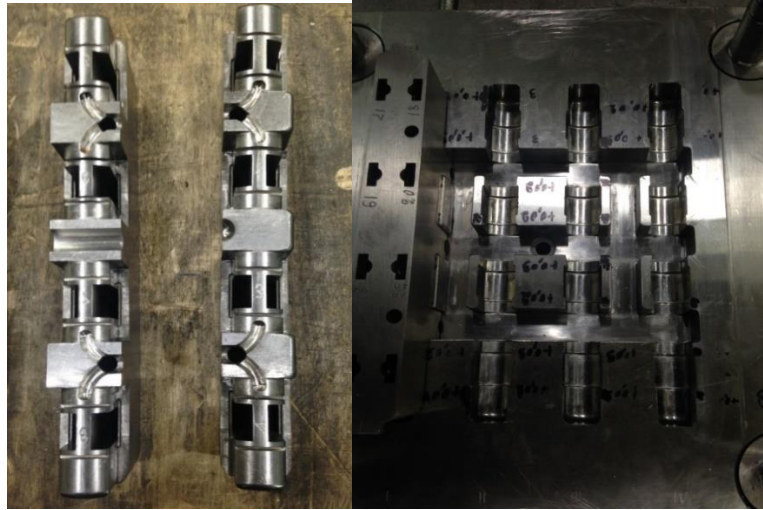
Формообразующие детали пресс-формы для изделия «Заглушка»
